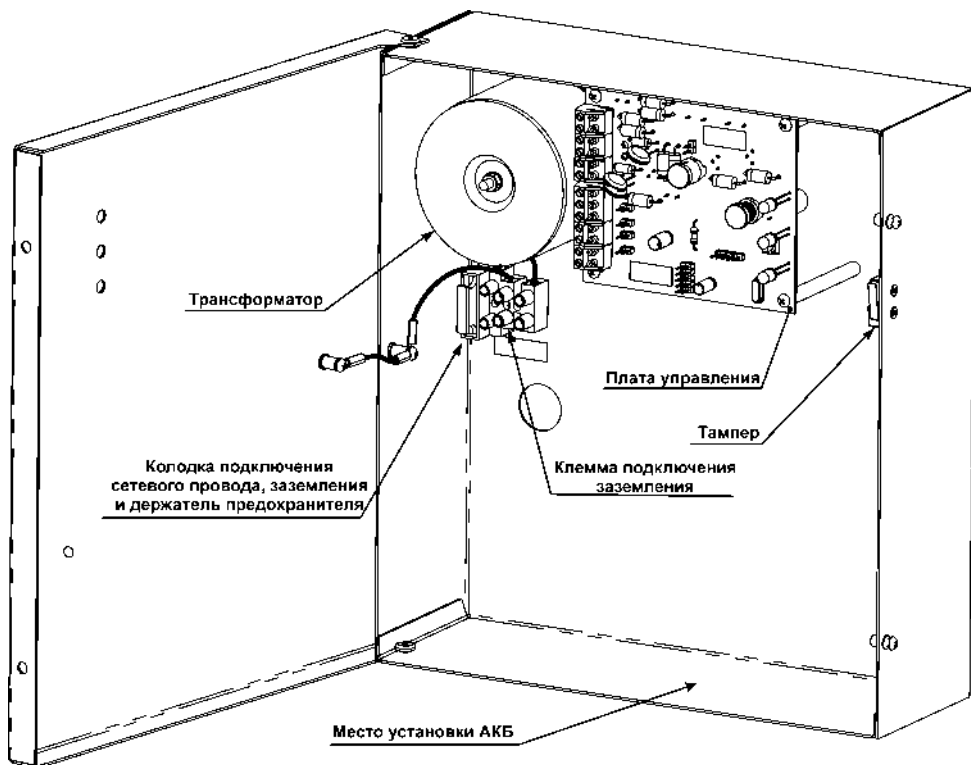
Вид прибора ИПС-12/2 с открытой крышкой
